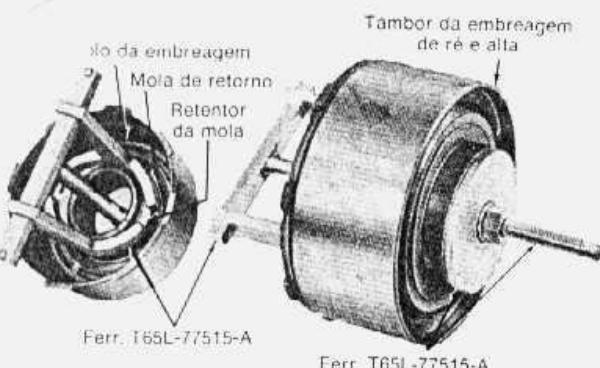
remoção ou instalação do anel de travamento da mola de retorno do êmbolo
